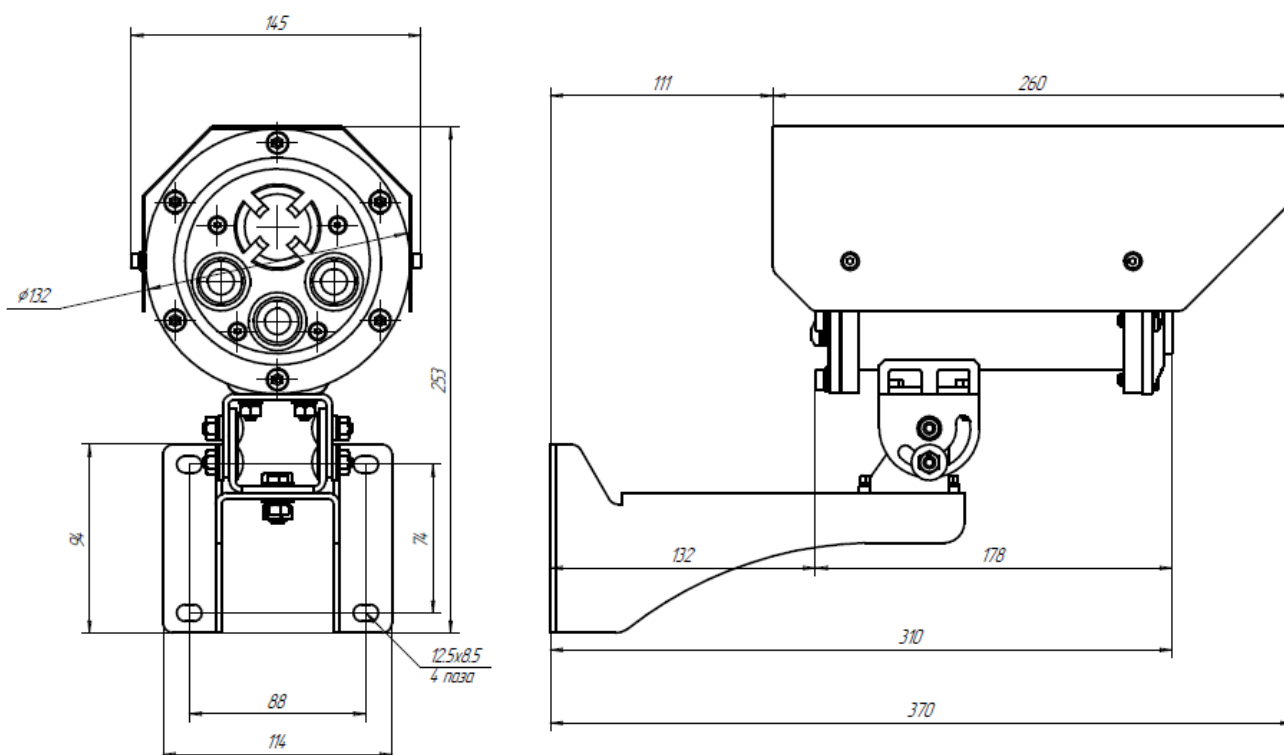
Габаритные размеры извещателя с крепежно-юстировочным устройством
